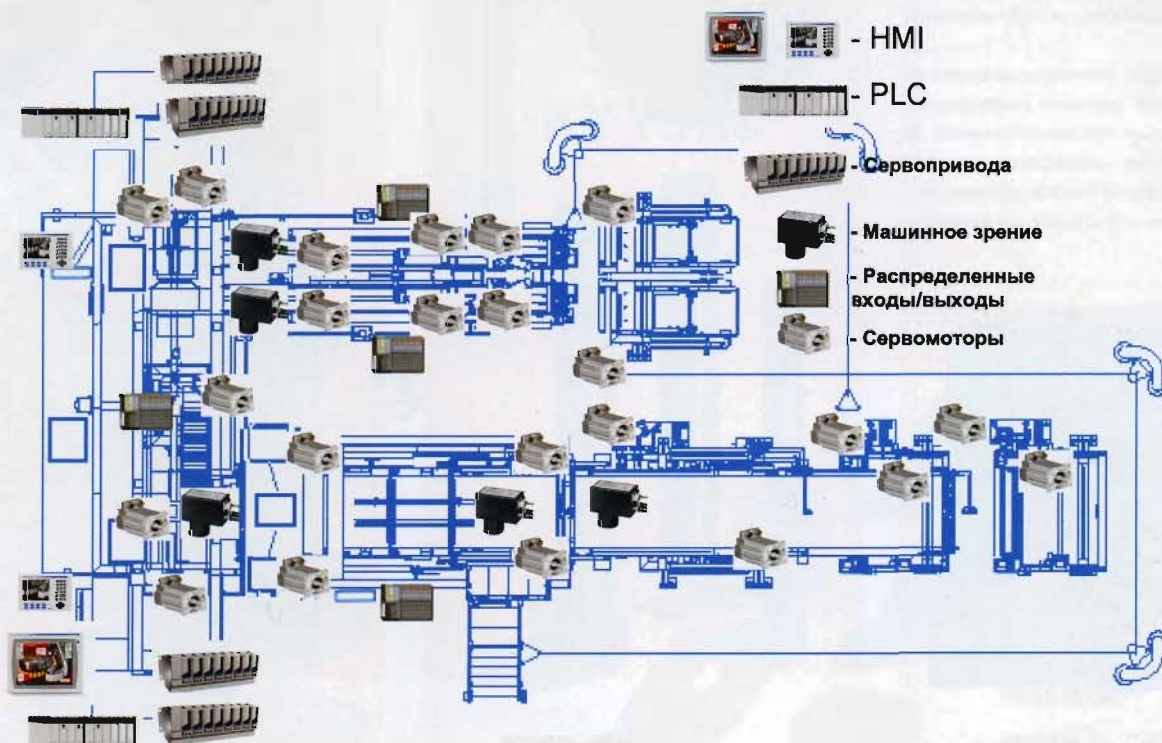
Расположение оборудования на сборочном станке (вид сверху)
